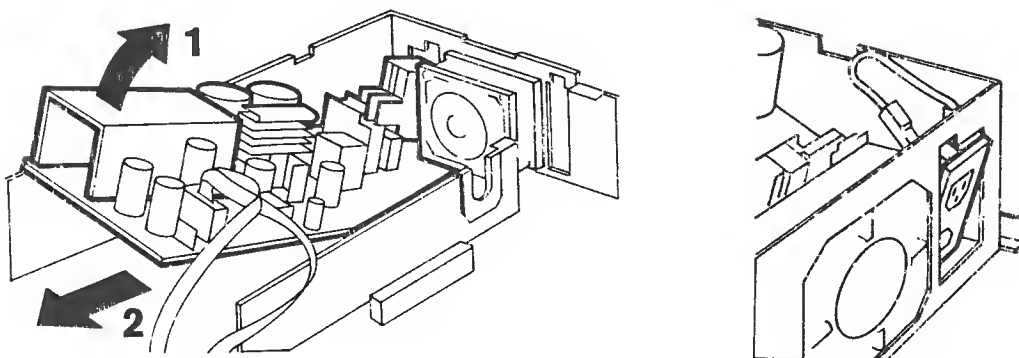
Stromversorgungsbaugruppe ausbauen
